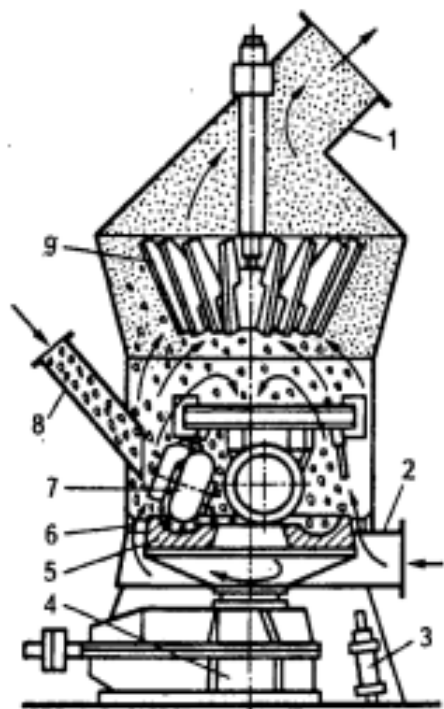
Роликовий млин: 1— вихідний патрубок; 2 – патрубок гарячих газів; 3 – гідропневматичний пристрій; 4 – привід; 5 – розмельна чаша; 6 – кільце з дюзами; 7 – валяння; 8 – завантажувальний патрубок; 9 – сепаратор
